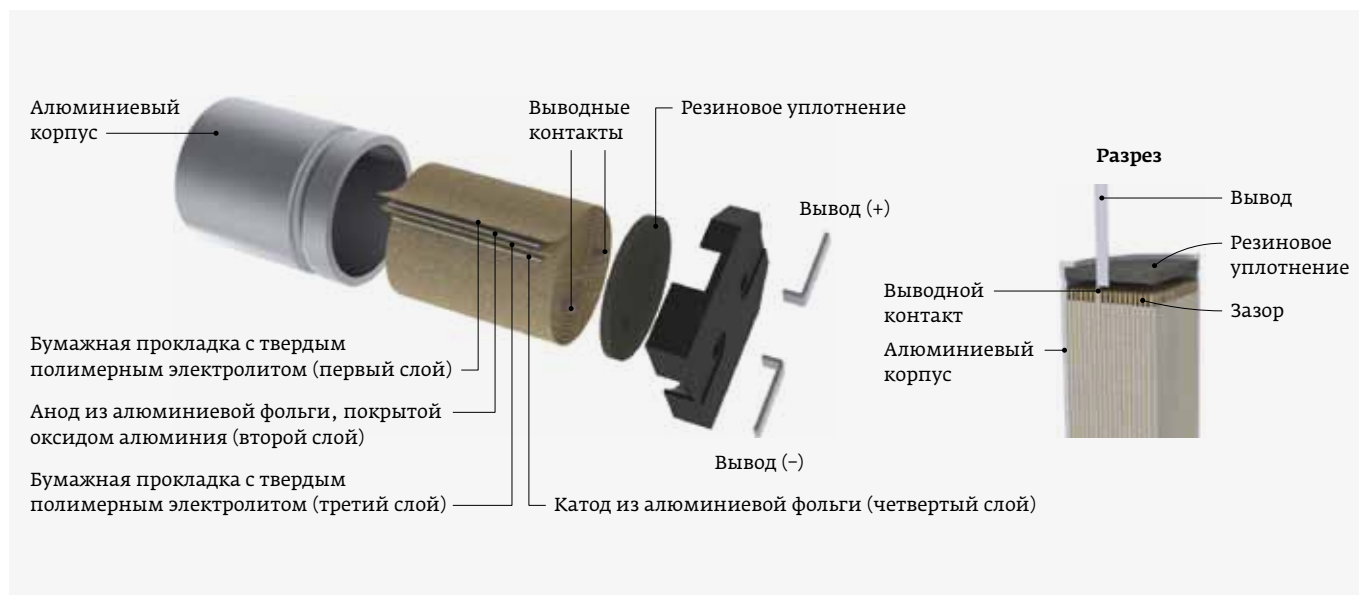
Конструкция алюминиевого полимерного SMD-конденсатора в круглом металлическом корпусе серии A768
